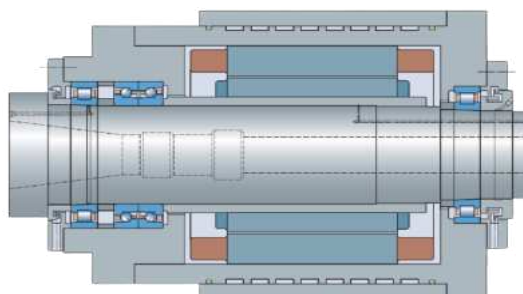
AP pentru freză CNC cu motor încorporat – variantă convențională [53]
